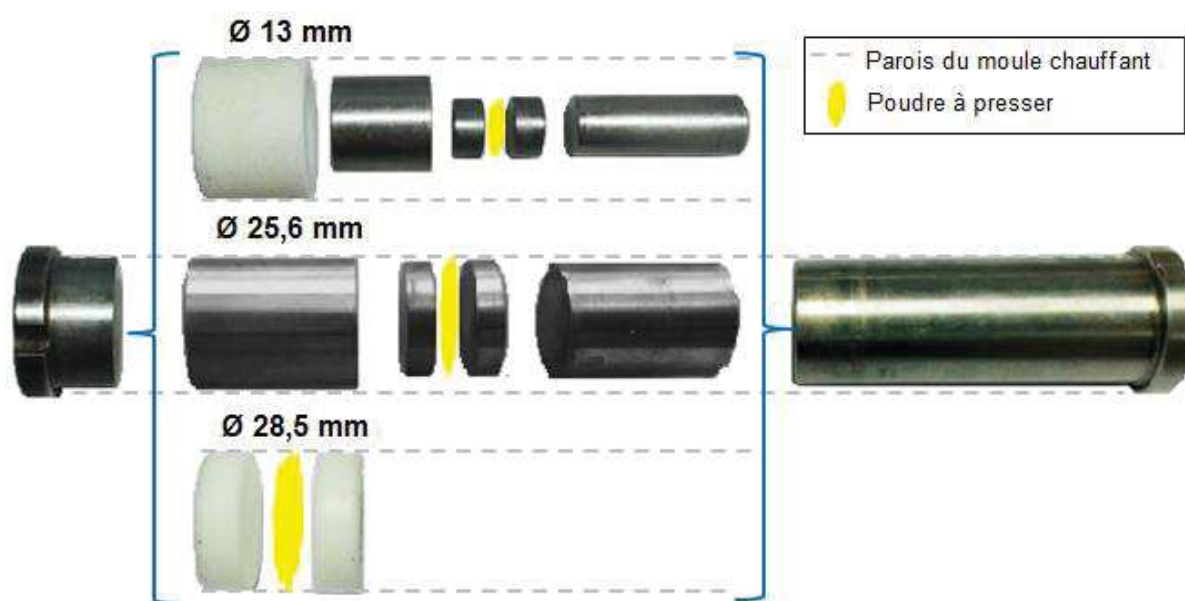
Photos des moules et pièces de pressage utilisés
